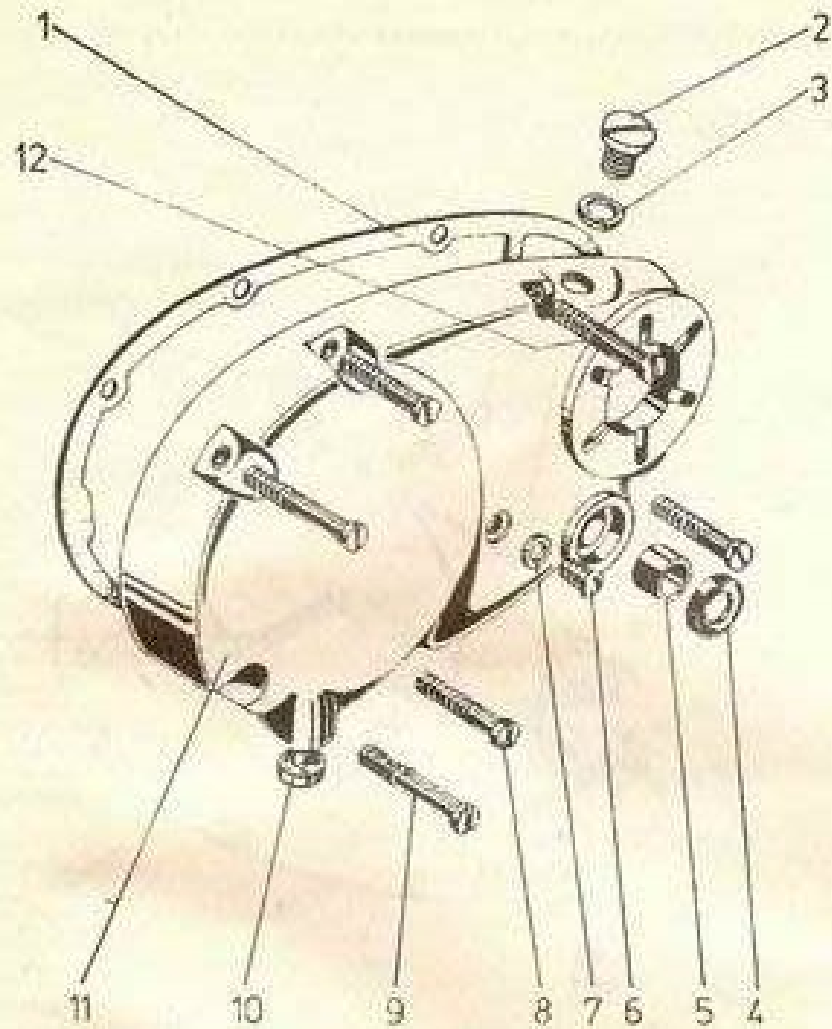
Крышка картера левая в сборе (B501.10.09.050)
